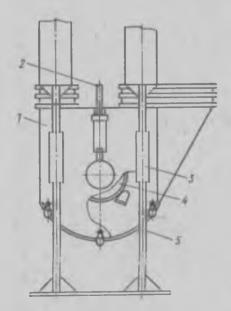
Башмак нории У1-УНС-20: 1 — корпус; 2 — винт; 3 — втулка; 4 — барабан; 5 — штанга
